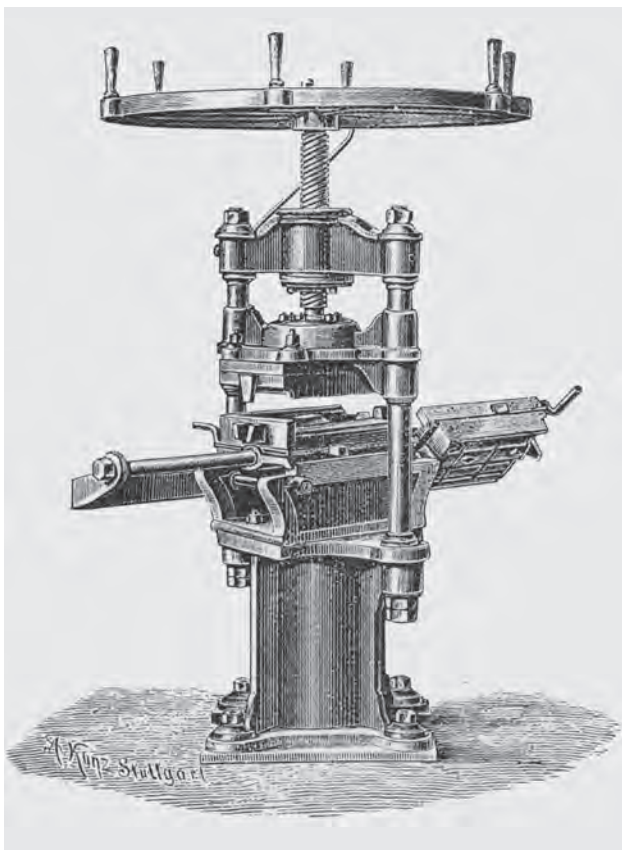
Handbetätigte Schraubenspindelpresse, um 1850
